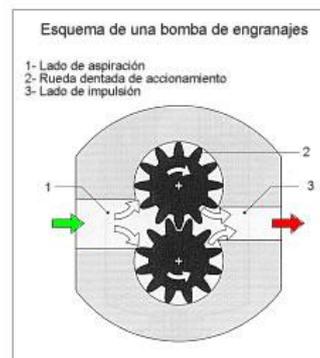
Bomba de engranajes (Bosch, 2011)
